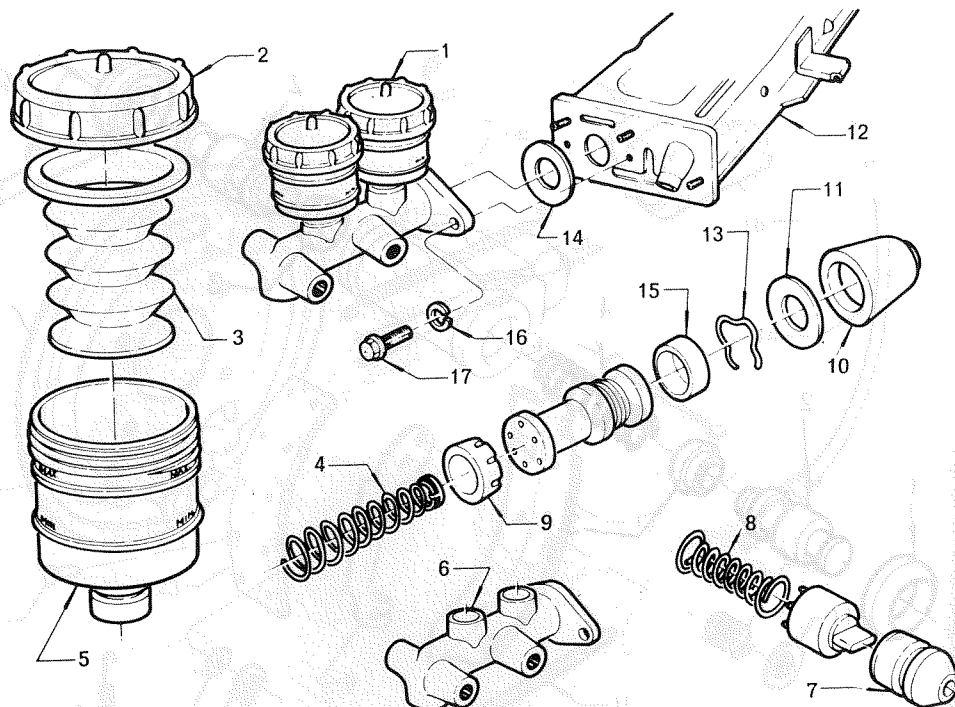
A — Cilindro ou burrinho mestre duplo (Bendix).
